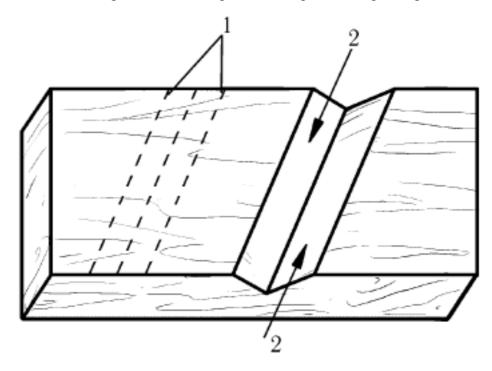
Выполнение двусторонней выемки, идущей по наклонной к направлению волокон заготовки (стрелками указано направление движения инструмента): I – разметка; 2 – грани выемки
